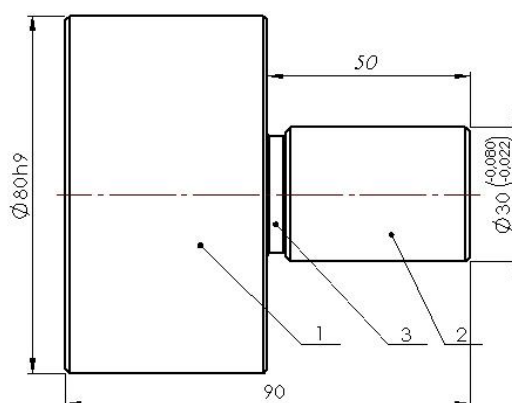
Контрольна заготовка для налаштування пристрою
